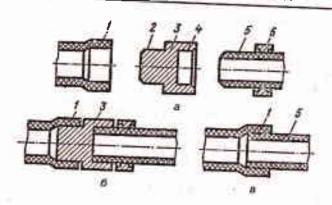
Технологический процесс контактной раструбной сварки:
